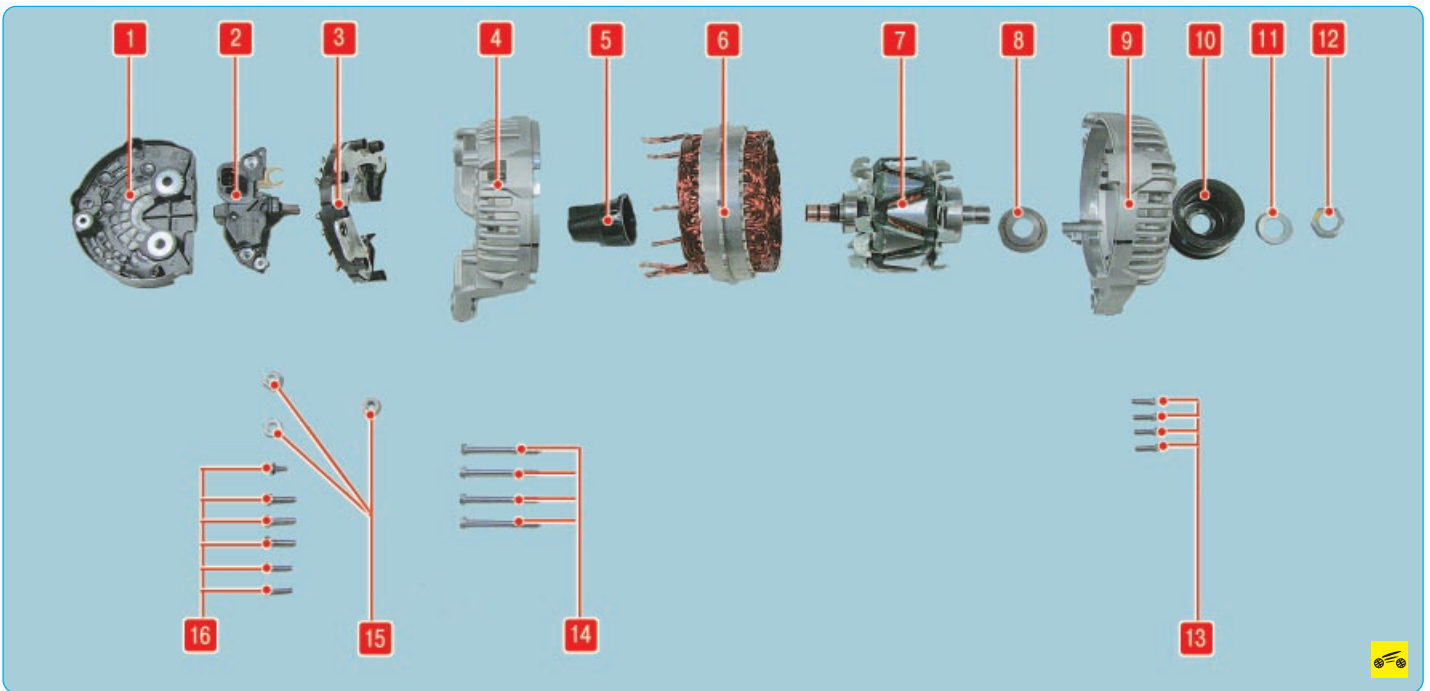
Детали генератора: 1 – защитный кожух; 2 – регулятор напряжения, объединенный со щеточным узлом; 3 – выпрямительный блок; 4 – крышка со стороны контактных колец; 5 – центрирующая втулка заднего подшипника ротора; 6 – статор; 7 – ротор; 8 – дистанционная шайба; 9 – крышка со стороны привода; 10 – шкив; 11 – стопорная шайба гайки крепления шкива; 12 – гайка крепления шкива; 13 – винты крепления пластины переднего подшипника вала ротора; 14 – стяжные болты; 15 – гайки крепления защитного кожуха; 16 – винты крепления регулятора напряжения и выпрямительного блока
